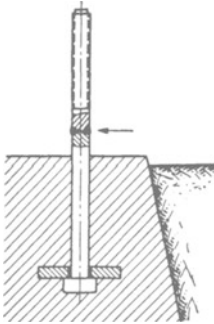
Schweißung eines Fundamentankerbolzens.
